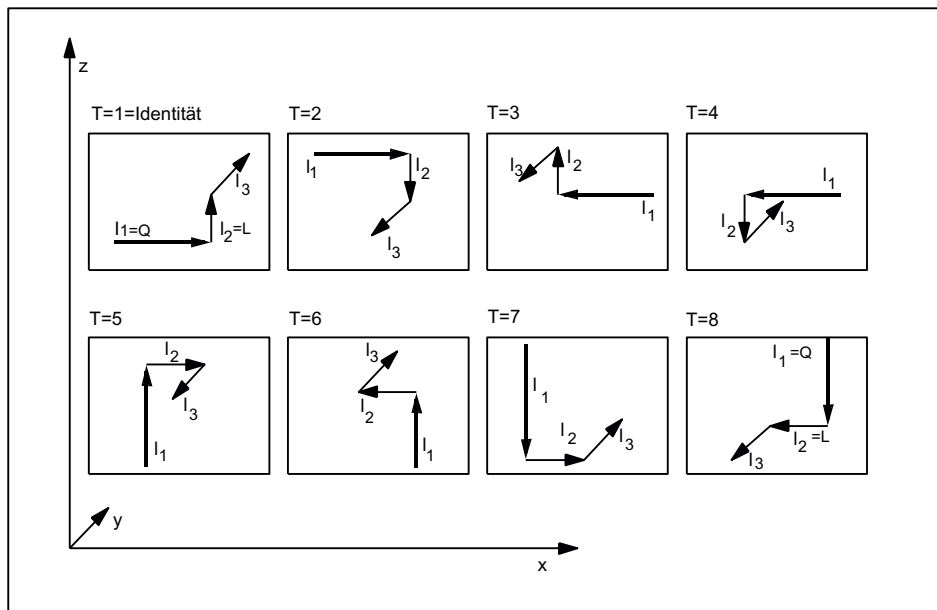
Die 8 definierten Transformationen (T = 1...8) für den Adapter mit G 18 und für ein Drehwerkzeug. Es werden die Zuordnungen der Werkzeuglängen l_1 , l_2 , l_3 auf die Geometrieachsen x, y, z gezeigt.
